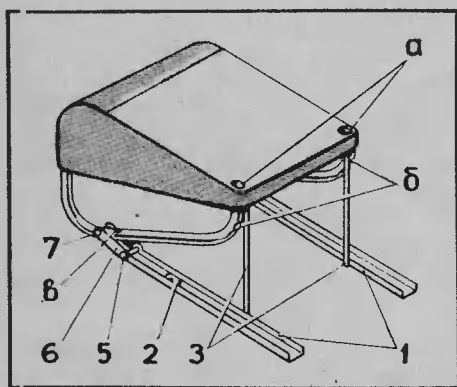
«Шагающее» сиденье в сборе: а — отверстия для шарниров спинки в рабочем положении; б — отверстия для штатных шарниров спинки при раскладке; в — отверстие под винт 4. Остальные позиции — те же, что и на рис. 6.
